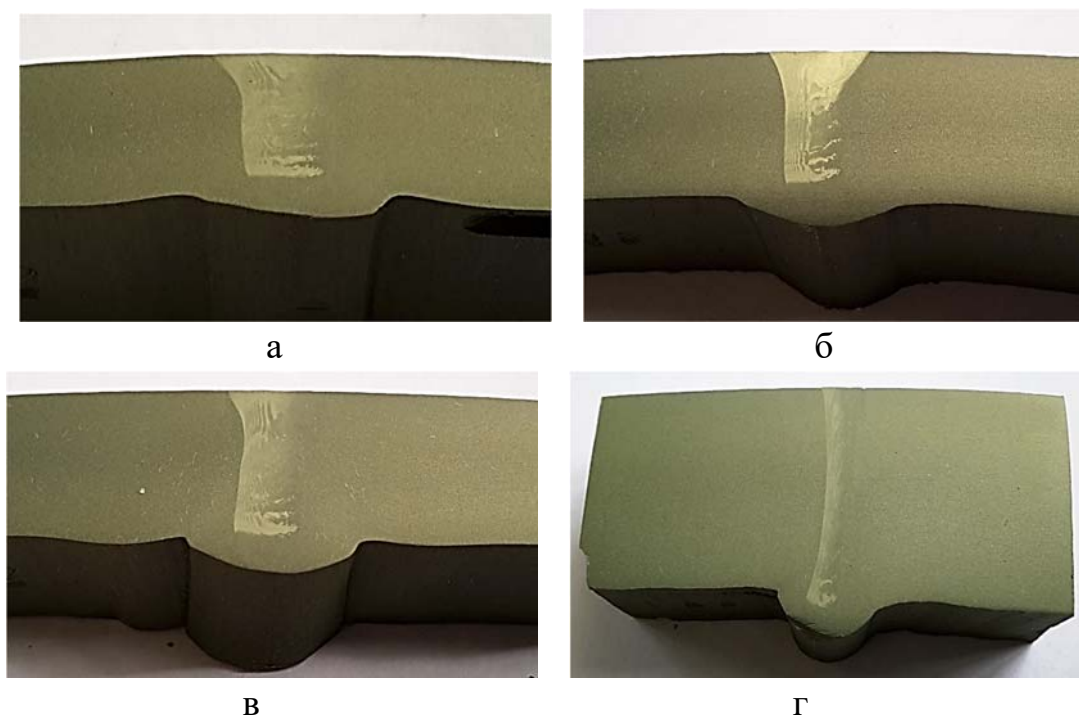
Изменение формы сечения сварного соединения по мере осадки сварной трубчатой заготовки из плава 1565чМ в нагретую форму
